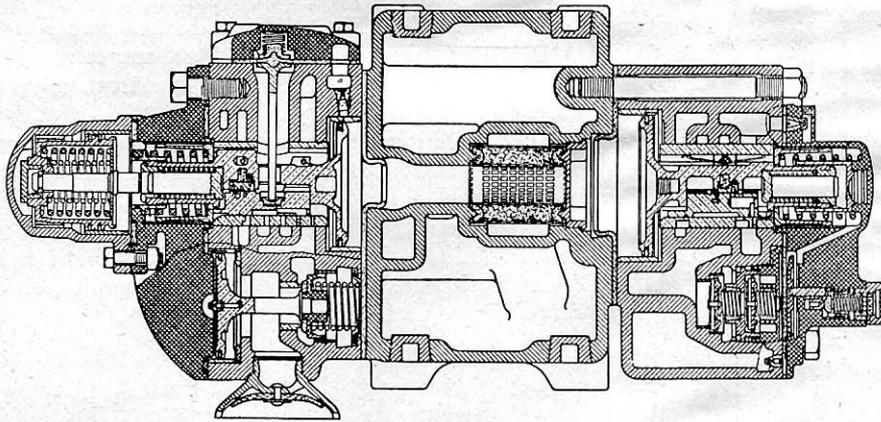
Amerikanisches Güterzugsteuerventil AB von Westinghouse mit Betriebsbremsventil und Schnellbremsventil.
